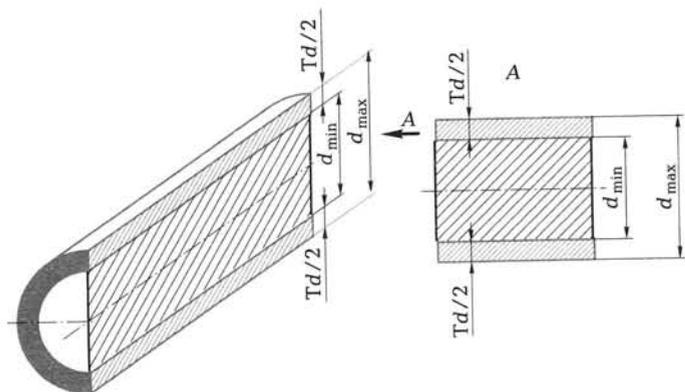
Симметричное расположение поля допуска вала
